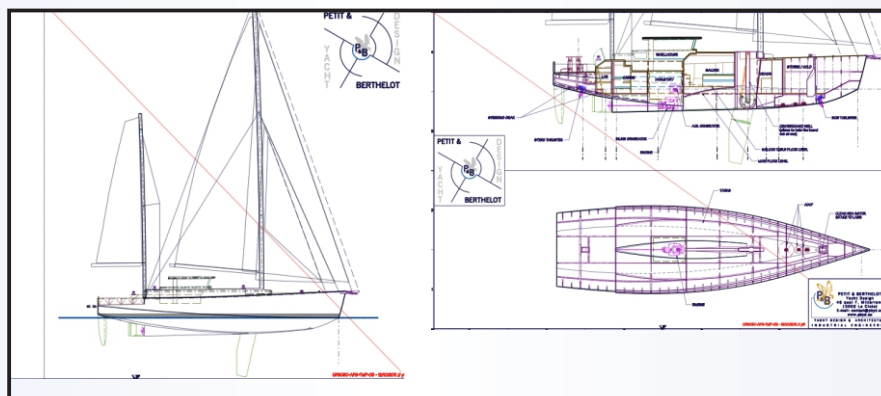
Plano estrutural, vélico e layout do veleiro ECO
